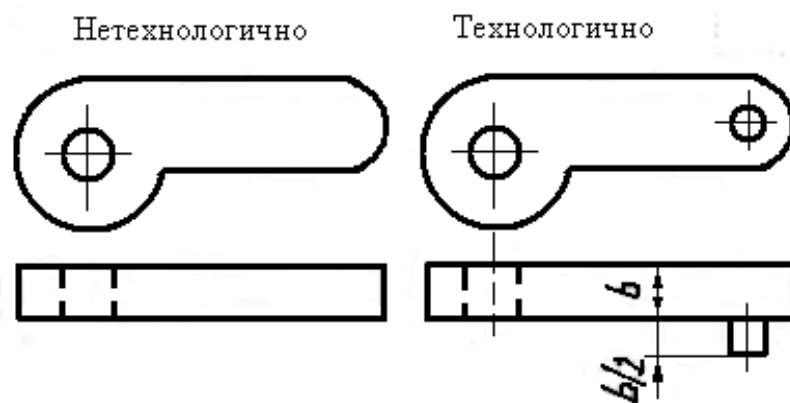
Дополнительный конструктивный элемент для удобства ориентирования детали
